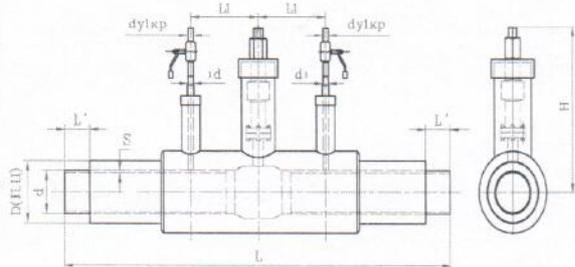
Кран шаровой с двумя кранами воздушника
